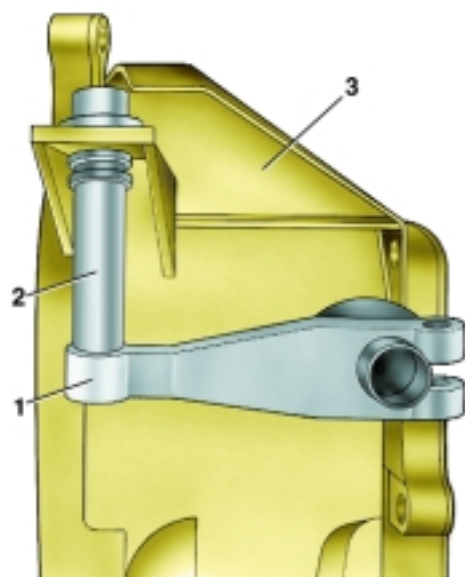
Установка транспортной распорки: 1 – наружный рычаг вала выключения сцепления; 2 – транспортная распорка; 3 – картер сцепления
